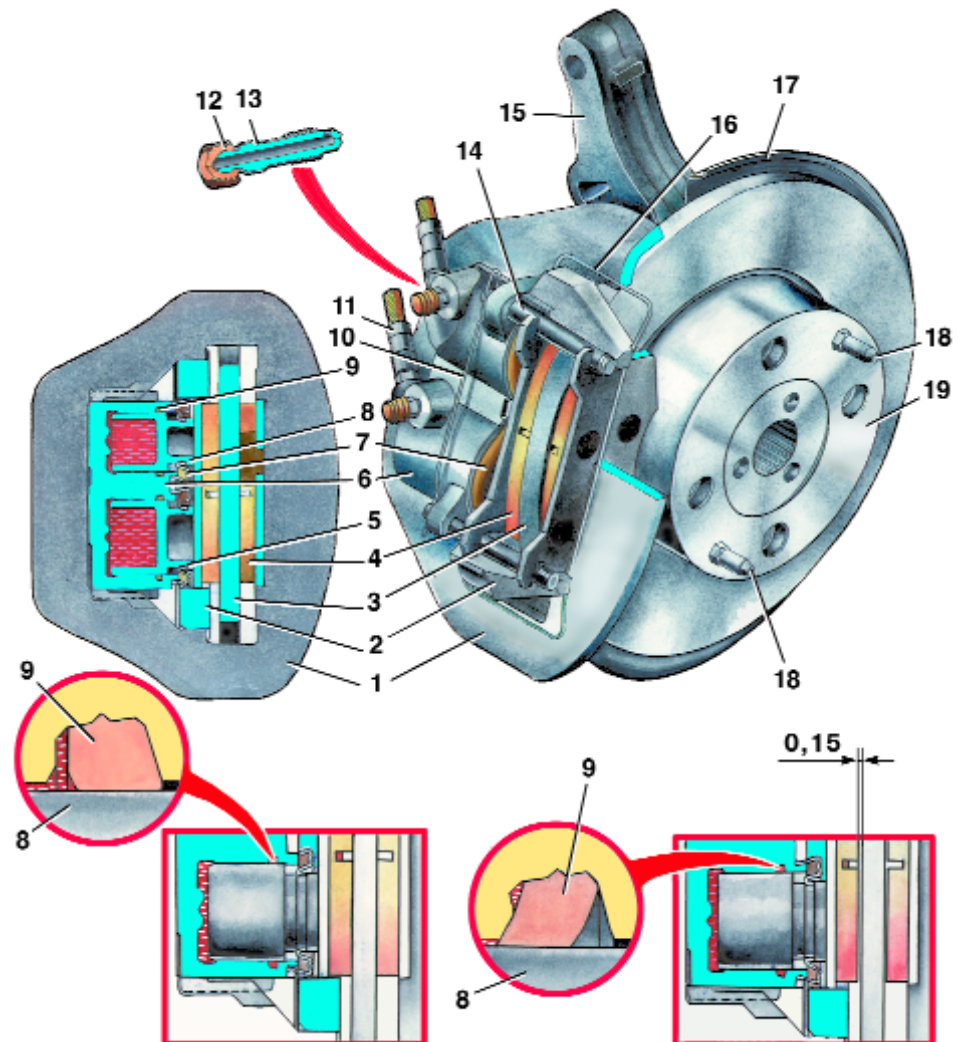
Тормозные механизмы передних колес: 1 – рама; 2 – суппорт; 3 – диск; 4 – колодка тормоза; 5 – поршень (большой); 6 – корпус цилиндра; 7 – грязезащитный чехол; 8 – поршень (малый); 9 – уплотнительное кольцо; 10 – фиксатор; 11 – гибкий шланг со штуцером; 12 – колпачок клапана; 13 – клапан выпуска воздуха; 14 – палец; 15 – поворотный кулак; 16 – пружина; 17 – щит; 18 – фиксаторы; 19 – ступица колеса
